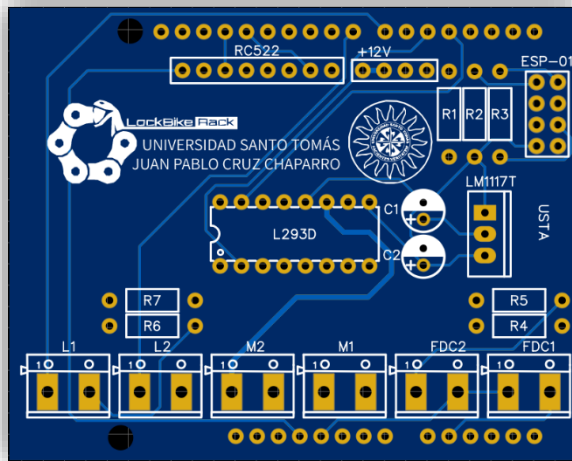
Diseño capa superior esquemático PCB, Proteus 8 Profesional – LockBikeRack
